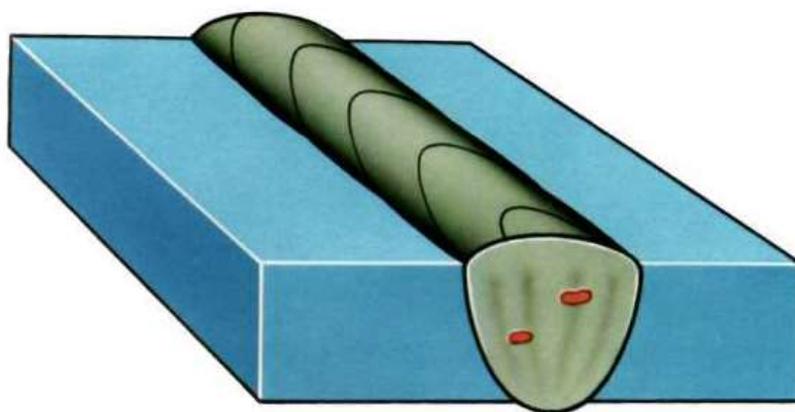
Дефект сварного шва по типу наличия оксидных включений
